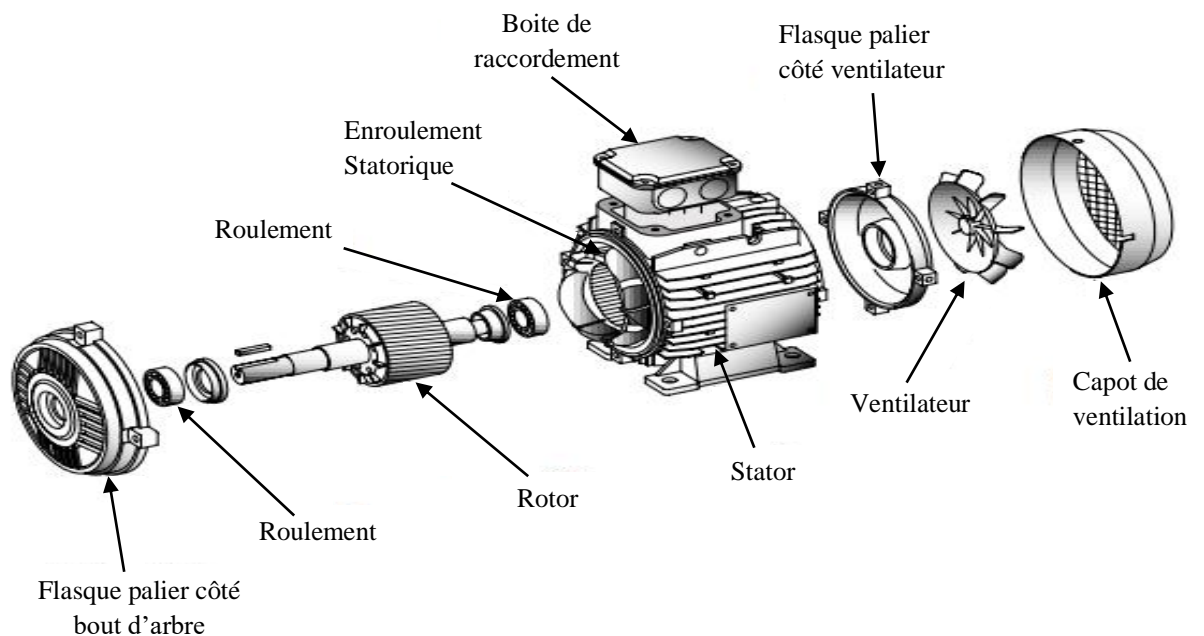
Vue éclatée d'un moteur asynchrone à rotor à cage
